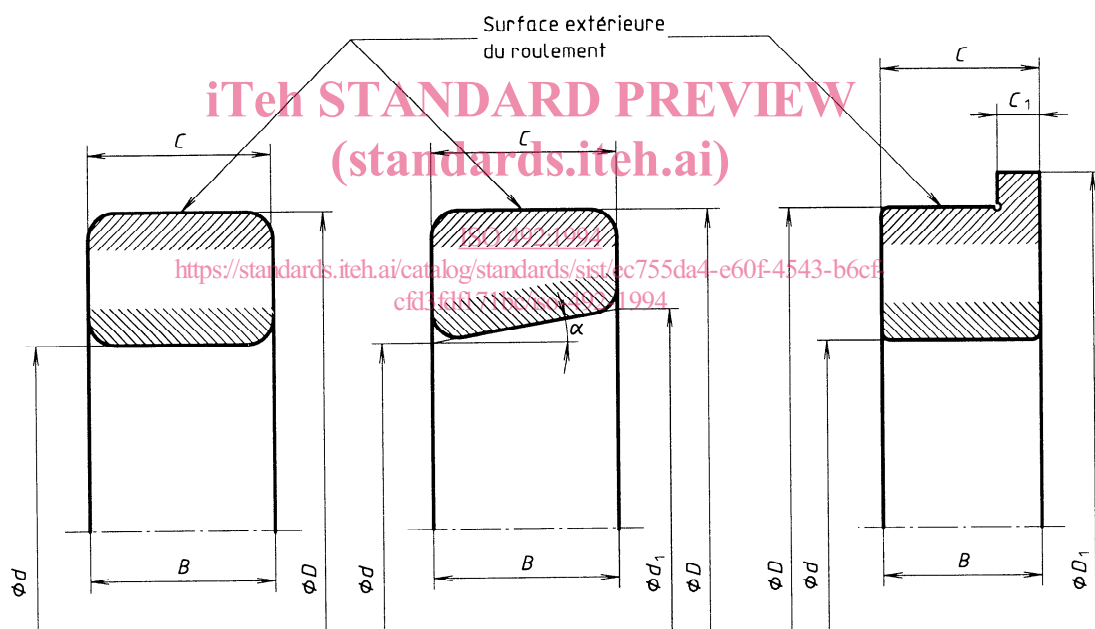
Symboles relatifs aux dimensions d'encombrement
